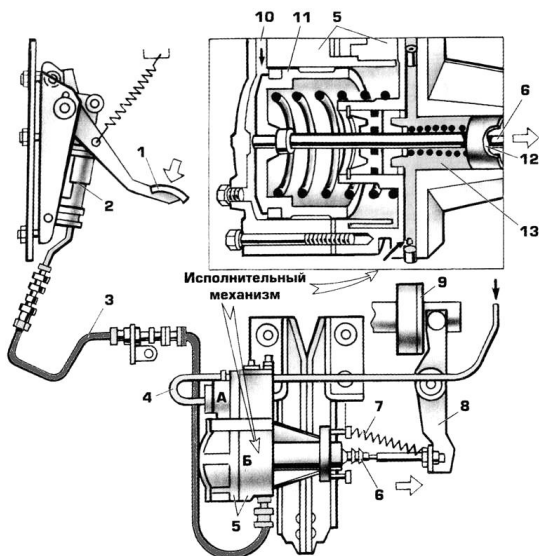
Пневматический усилитель привода сцепления КамАЗ:
